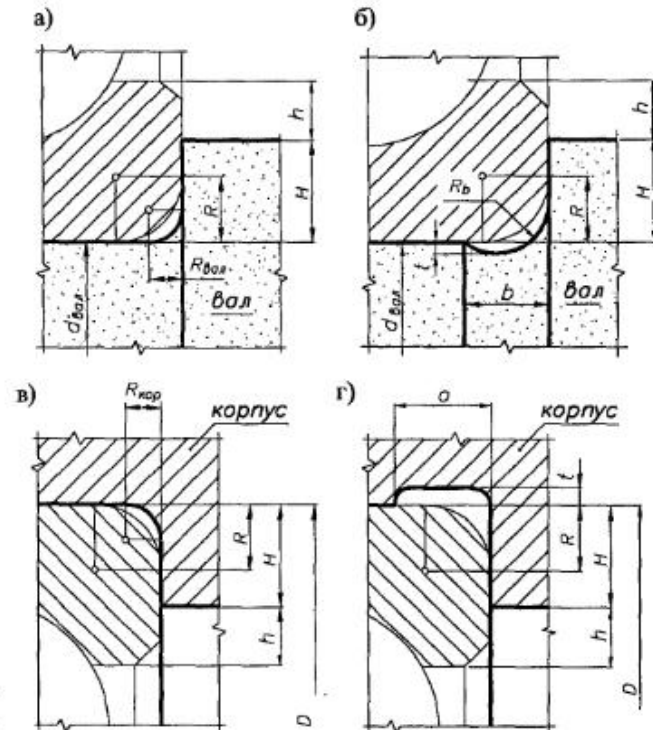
Радиусы закруглений и размеры подточек: а), б) для вала; в), г) для корпуса
